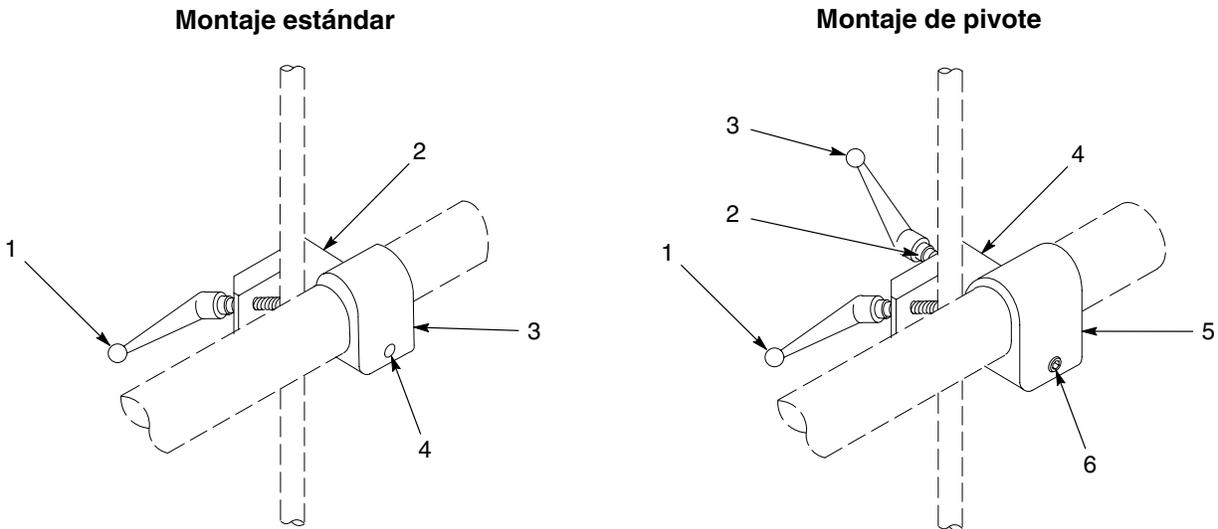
Montajes en barra de pistola para pistolas de montaje en tubo
